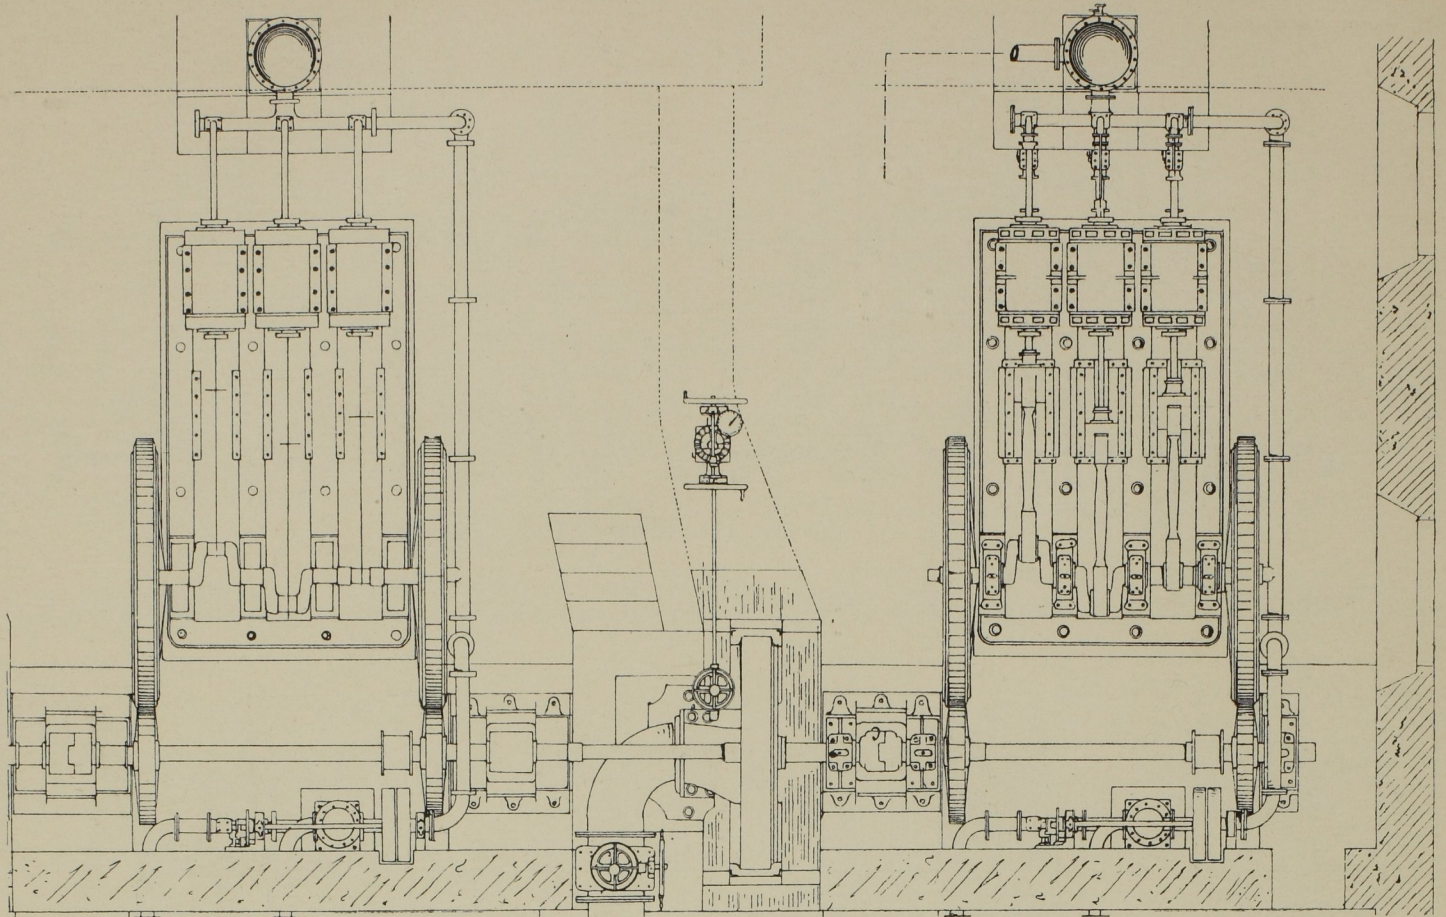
Grundriss der Kompressoren-Anlage.
